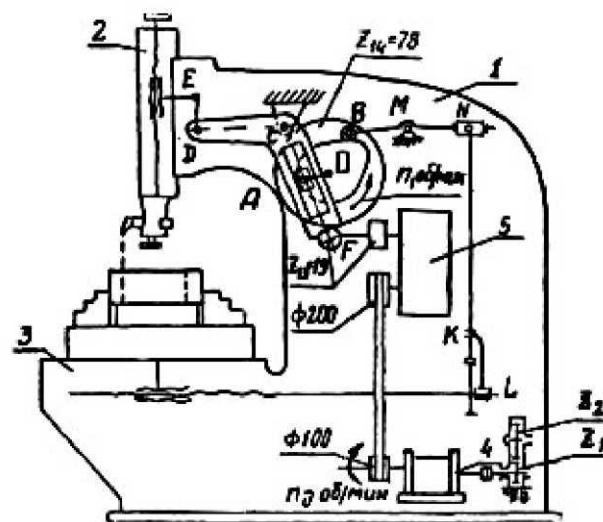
Общий вид долбежного станка с качающейся кулисой
